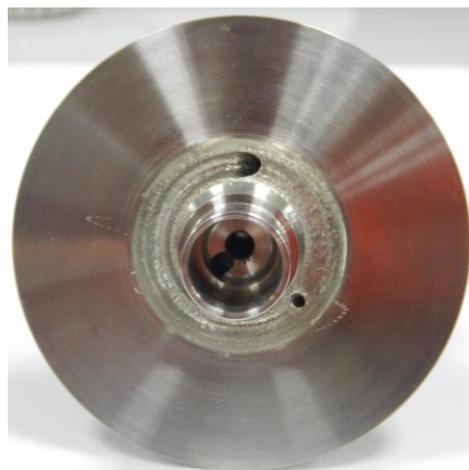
Корпус смесительной головки камеры двигателя РД840
